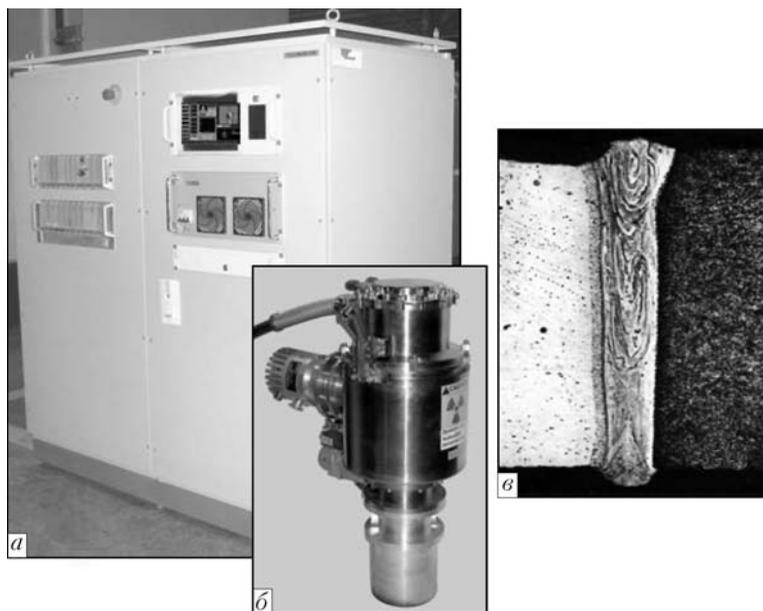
Источник питания ЭЛА-120/6 (а), сварочная пушка со снятой рентгеновской защитой (б) и макроструктура сварного соединения сталей Р6М5 + 50ХФА толщиной 1,35 мм (в) при скорости сварки 7,8 м/мин; ускоряющем напряжении 120 кВ; токе пучка 12,5 мА; ширине литой зоны в верхней и корневой части шва соответственно 0,35 и 0,25 мм
